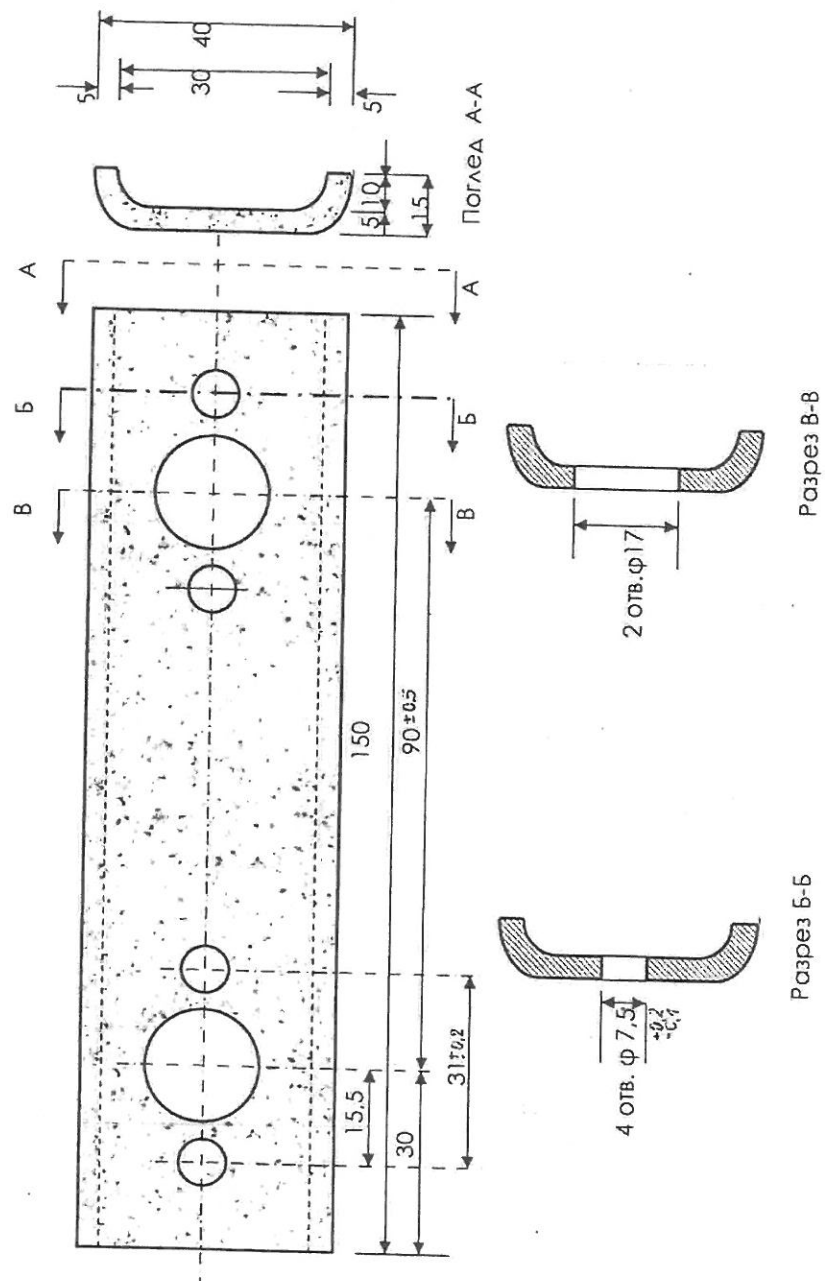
Арматурен пакет и анкерна планка – вид I.
